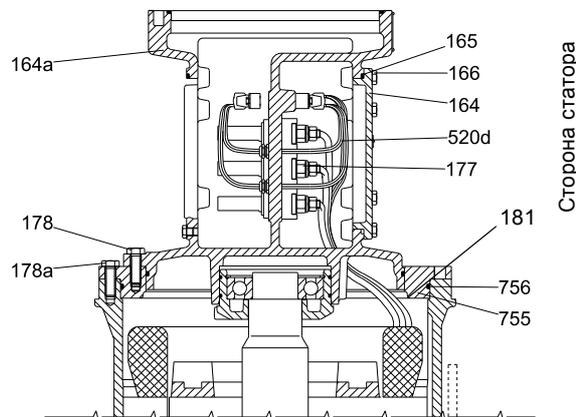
Клеммная коробка (без верхней крышки электродвигателя), типоразмер 74
